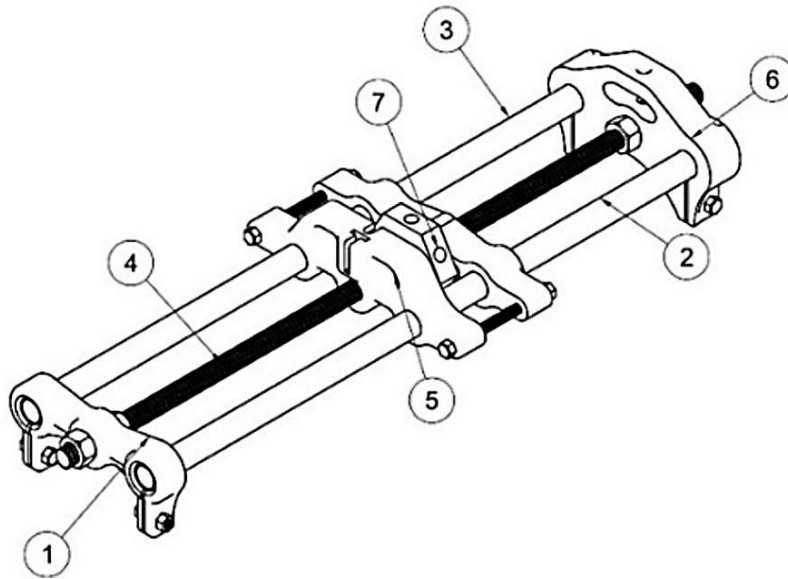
Общий вид станда: 1 – стойка; 2, 3 – направляющие; 4 – шпилька; 5 – каретка; 6 – стойка с креплением под измерительный прибор; 7 – колесо с гайкой
